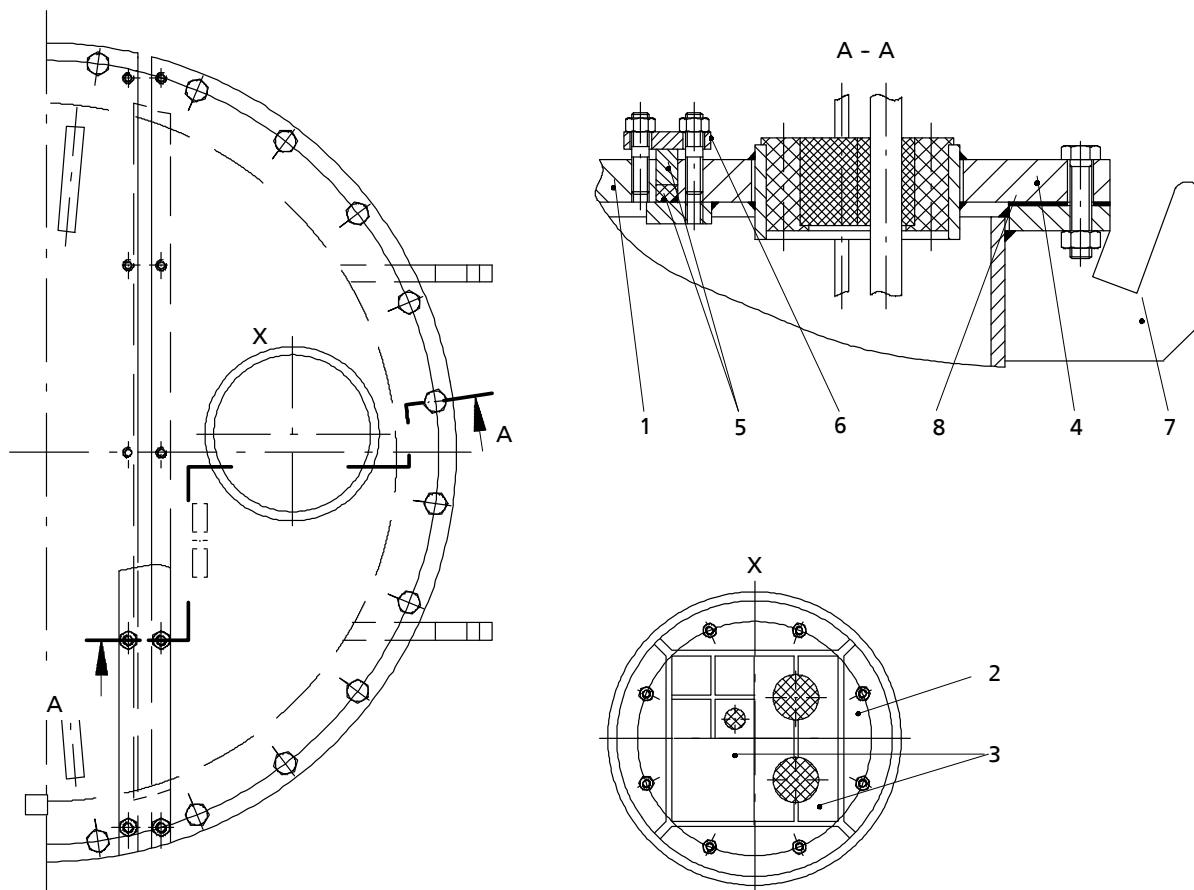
Ausführungsvariante: mit Stoprahmen (bis 1 bar)
